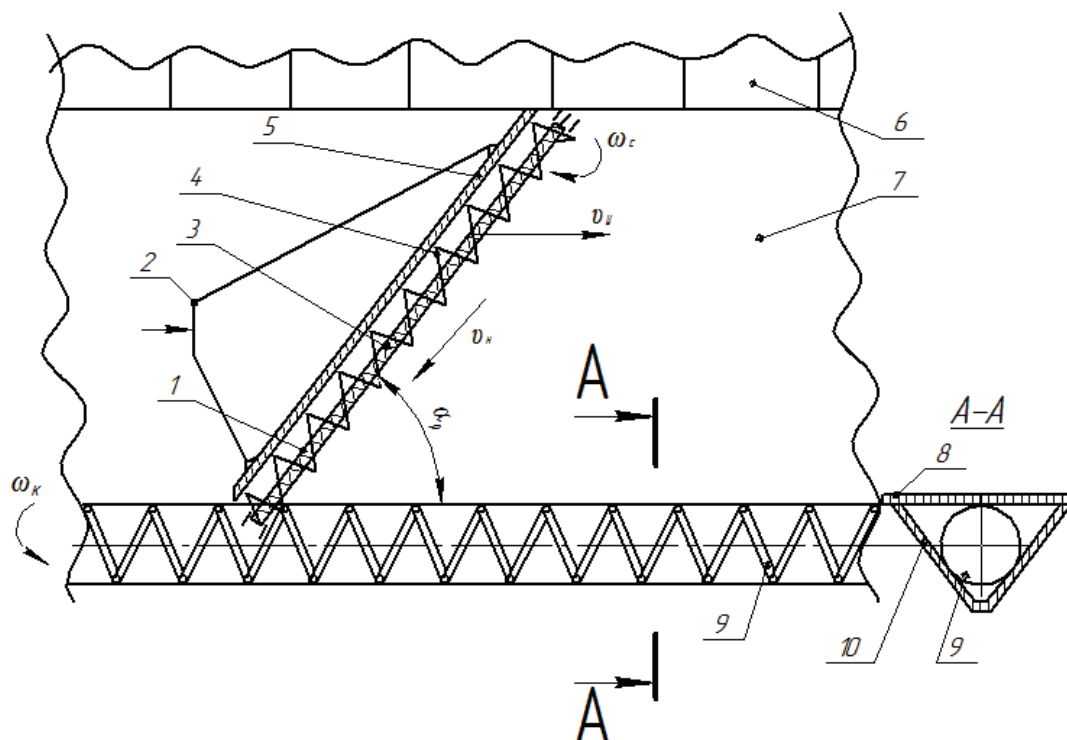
Схема компоновки устройства : 1 - труба; 2 - рамка для передвижения устройства; 3 - спираль внутренний; 4 - спираль рабочий; 5 - отражатель; 6 - кормушка; 7 - стоила; 8 - решетка; 9 - спираль продольного канала; 10- обшивка канала (желоба)
